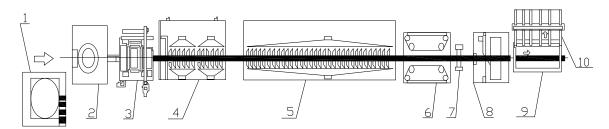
Технологическая схема оборудования для производства полиэтиленовых труб: I — бункер-накопитель полиэтиленового гранулята; 2 — экструдер; 3 — матричная головка; 4 — вакуумная калибровочная ванна; 5 — ванна водяного охлаждения; 6 — тянущее устройство; 7 — коронатор; 8 — отрезное устройство; 9 — накопитель-перекладчик; 10 — стеллаж-накопитель — контроль качества трубы
